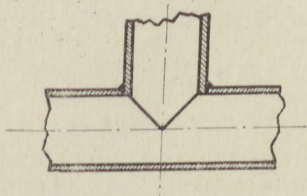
Einschweißen eines Rohrstützens.
